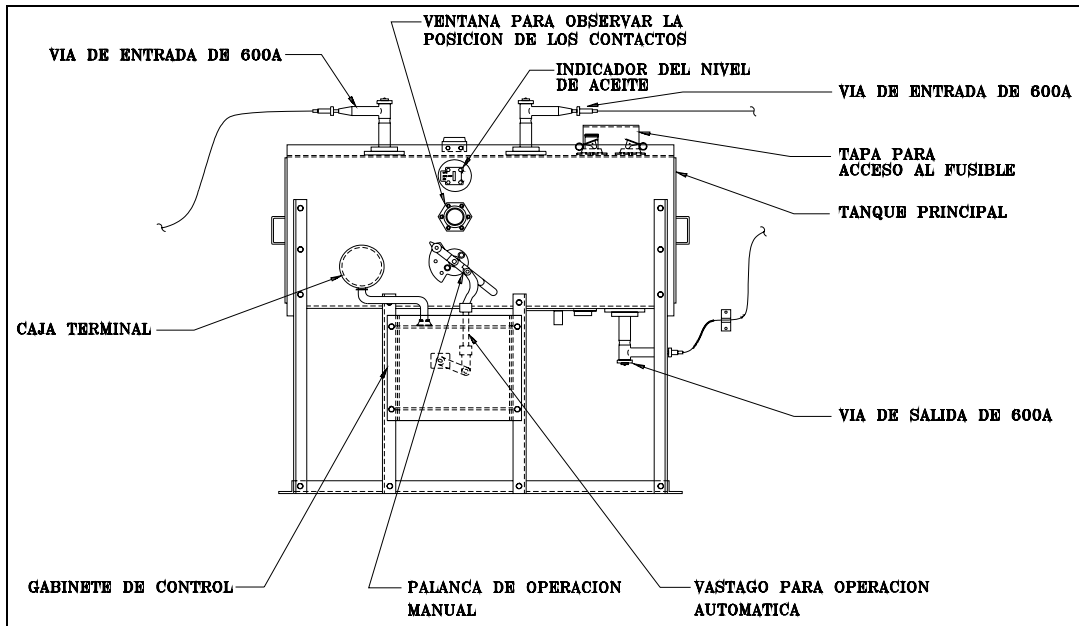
Vista Exterior Seccionador AVRAD
